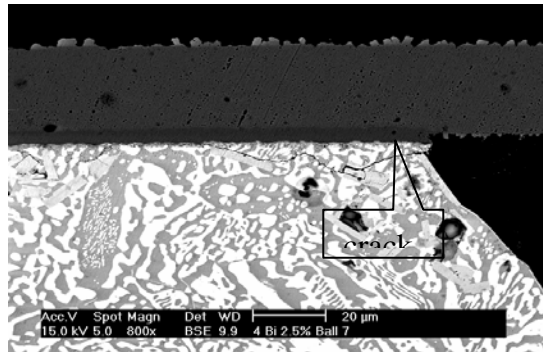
Sn-58Bi BGA 構裝模組在 PCB 反覆彎曲作用下，在最角落錫球應力集中處產生裂紋並沿AuSn₂邊界成長的情形
